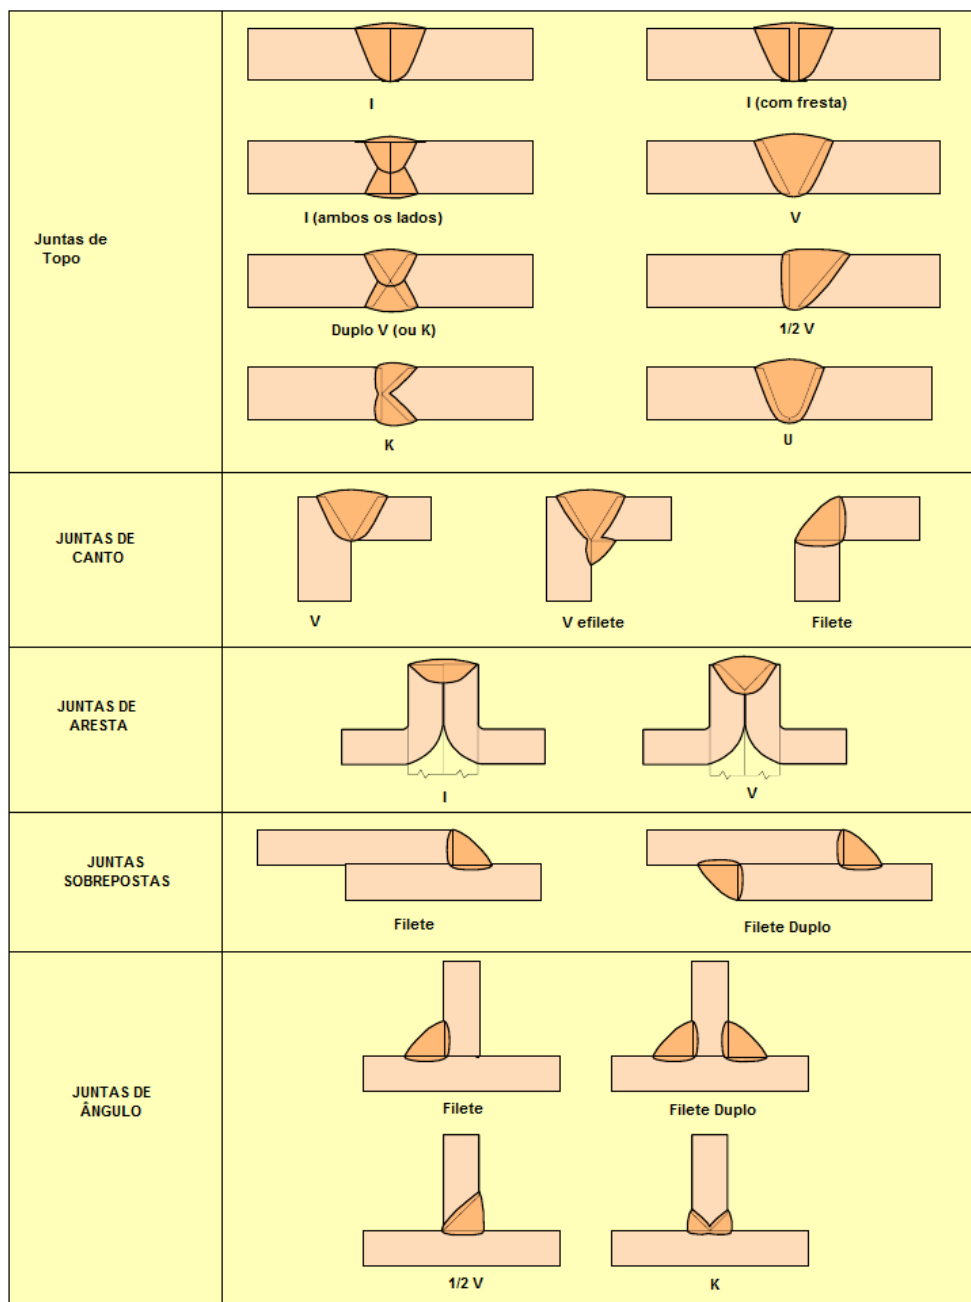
Exemplo de soldagem de filetes e seus símbolos
